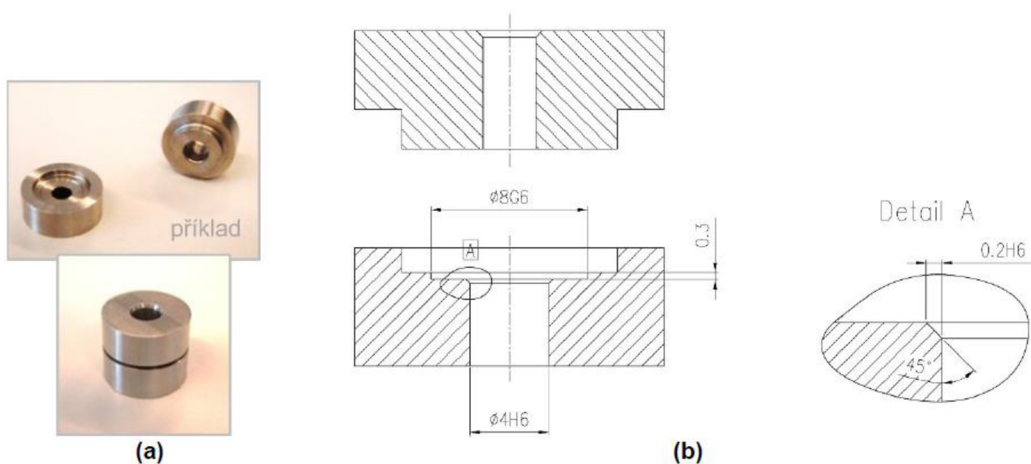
Schéma Small Punch Testu upraveno dle [5]
